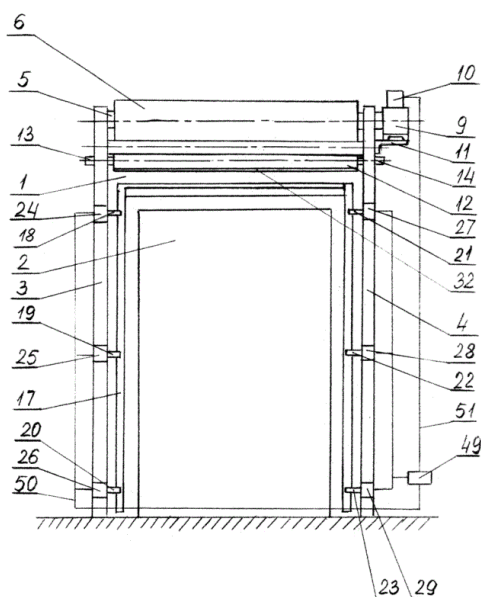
Схематичный вид рабочего состояния двери двойного действия
